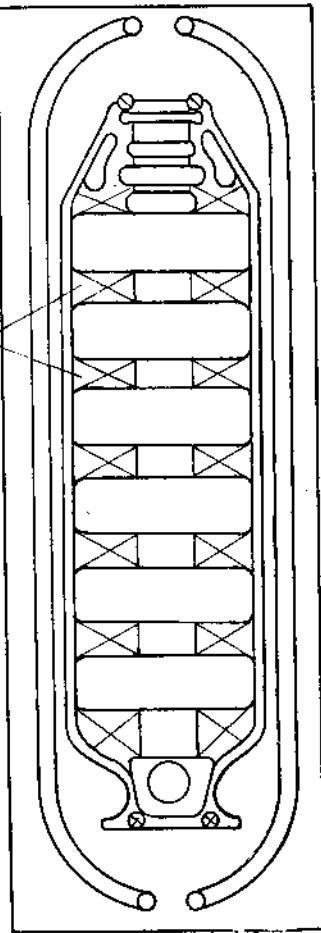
а. Схема формовки нижнего картера фланцем вверх, подвод металла с боков под прибыль.
